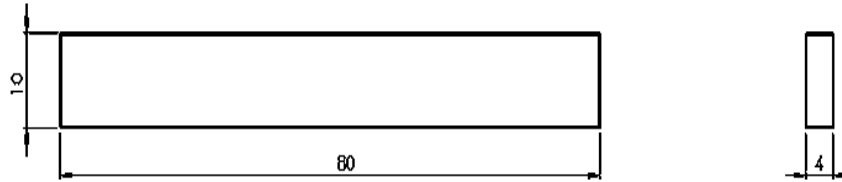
Croquis de una probeta diseñada para el ensayo de flexión.
